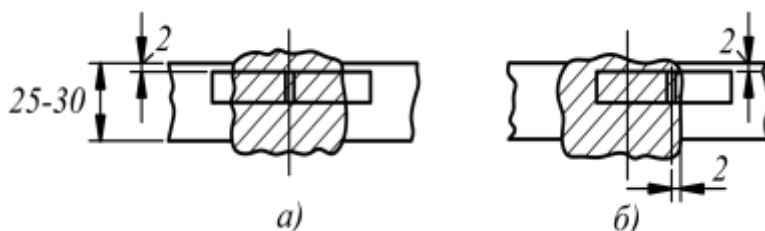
Схема вирізки і розташування надрізу для випробування зразків на ударний згин із проби стикового з'єднання при випробуваннях для електрошлакового зварювання і дугового зварювання з примусовим формуванням і газовим захистом :
